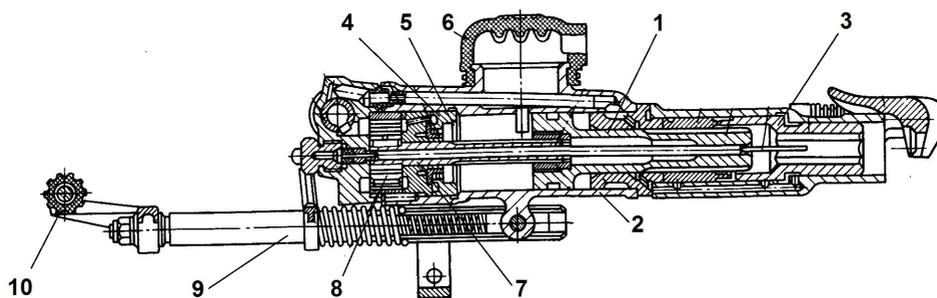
Типовая конструкция переносного пневматического перфоратора
